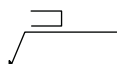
Схема условного обозначения сварного шва
